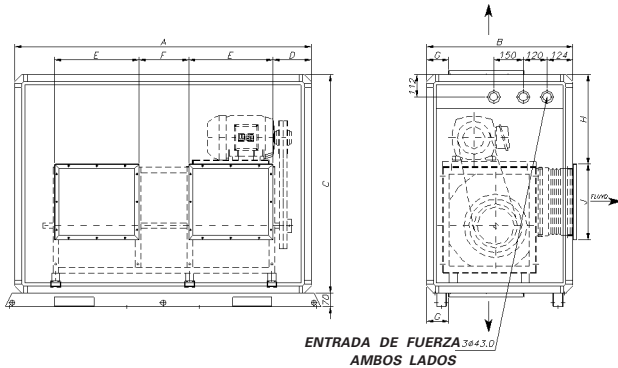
Dimensiones Módulo Ventilador 050 a 100 - Backward-Curved
